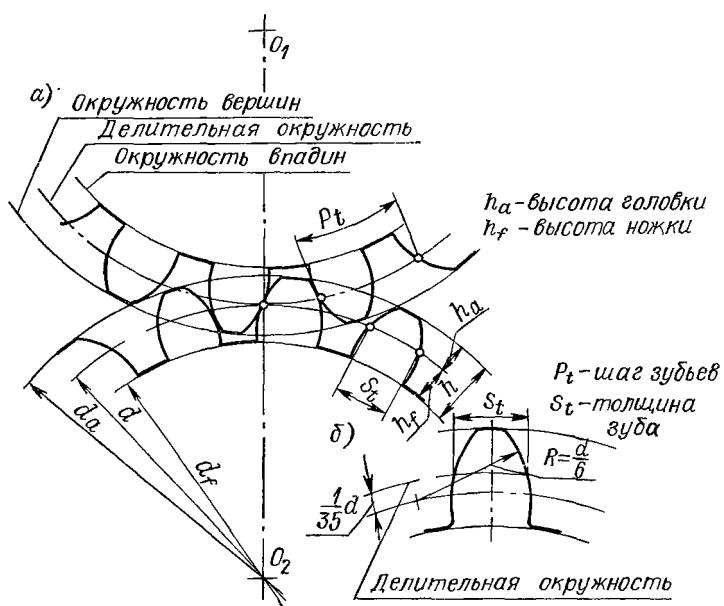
Упрощенное изображение зубьев: а — элементы зубчатого зацепления; б — профиль зуба
